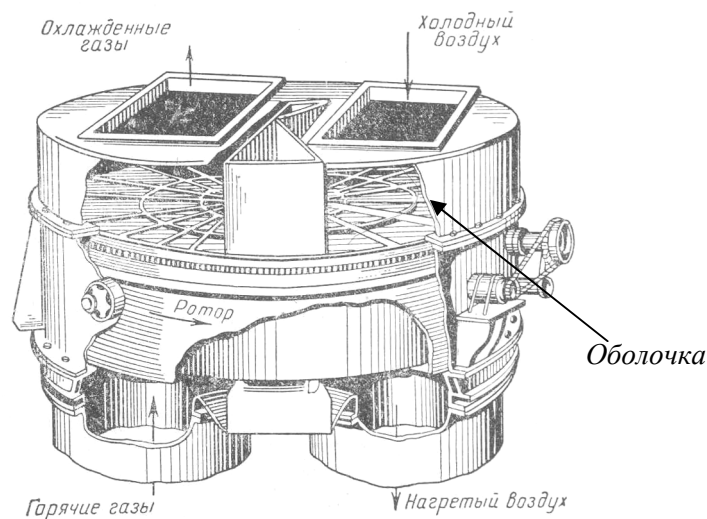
Цилиндрический корпус регенеративного воздухоподогревателя
